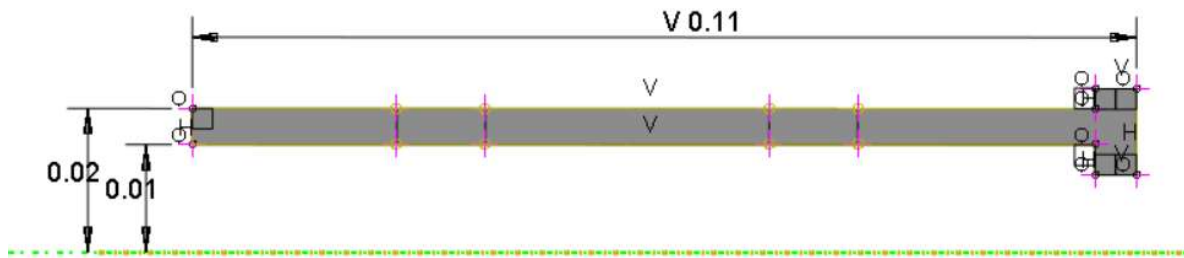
Dimensiones del cilindro del modelo del disipador.
